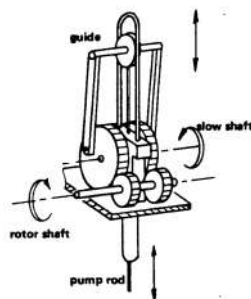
Sistema de transmisión de dos varillas impulsoras excéntricas con caja de engranajes simétrica. Fuente: "Wind Pumping Handbook" por Joop van Meel y Paul Smulders
